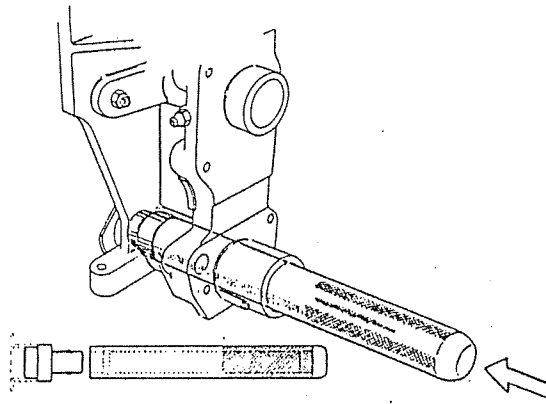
Verktyg för urpressning av inre bussning i lagerkonsol, främre fjädring. (Dorn Saab 92-32 och skaft Saab 92-30.)
